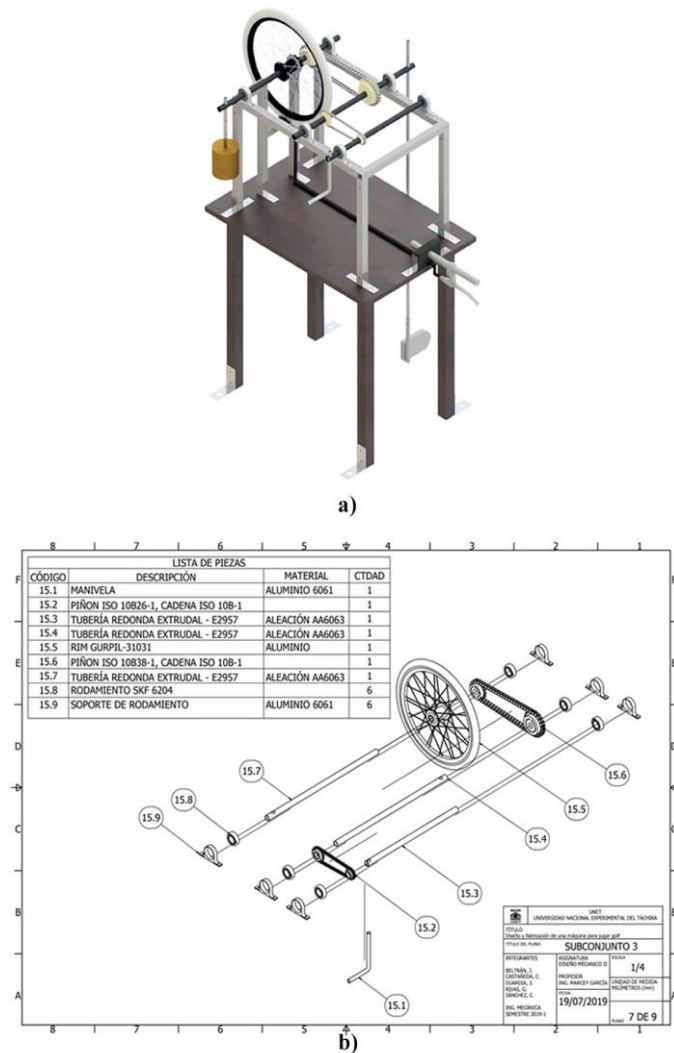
Modelado CAD de una máquina para jugar golf: a) Modelo 3D; b) Plano con el despiece de un subsistema de la máquina. Fuente: El autor.
